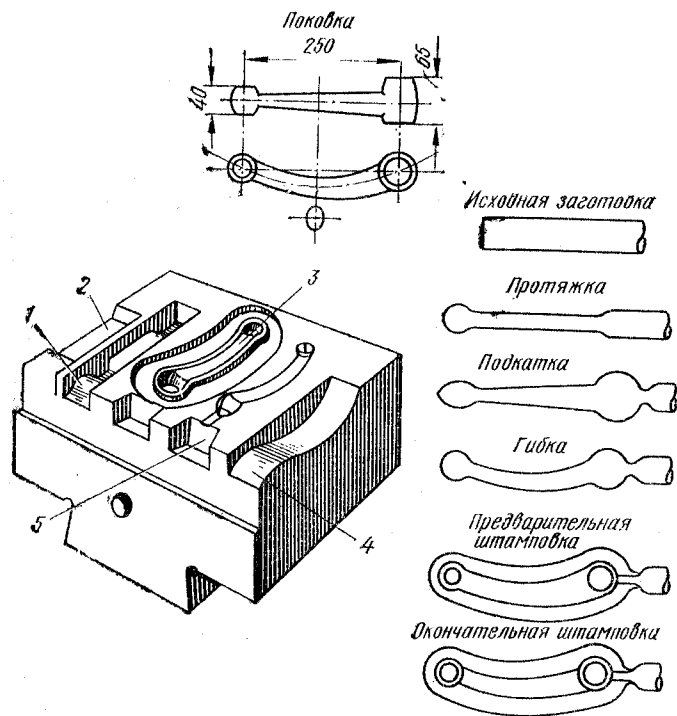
Многоручьеv штамп для штамповки поковки ручага из прутка и технологические переходы:
